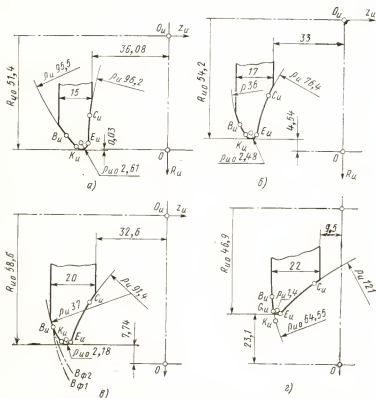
Профили дисковой фрезы для обработки винтовых канавок у цилиндрических фрез, рассчитанные при различных значениях параметров ее установки
